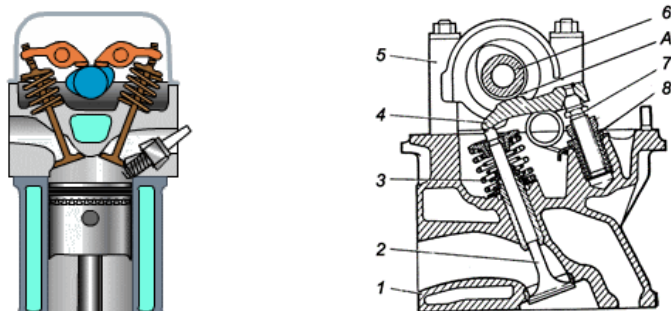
ГРМ з верхнім розташуванням розподільних валів: 1 – головка циліндрів; 2 – клапан; 3 – ущільнюючий ковпачок; 4 – одноплечий важіль клапана (рокер); 5 – корпус опор розподільного валу; 6 – розподільний вал; 7 – регулювальний гвинт; 8 – контргайка; А – тепловий зазор між важелем і кулачком розподільного валу
